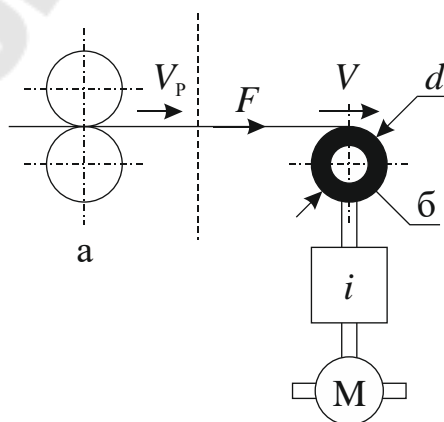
Кинематическая схема намоточно-размоточного механизма.
